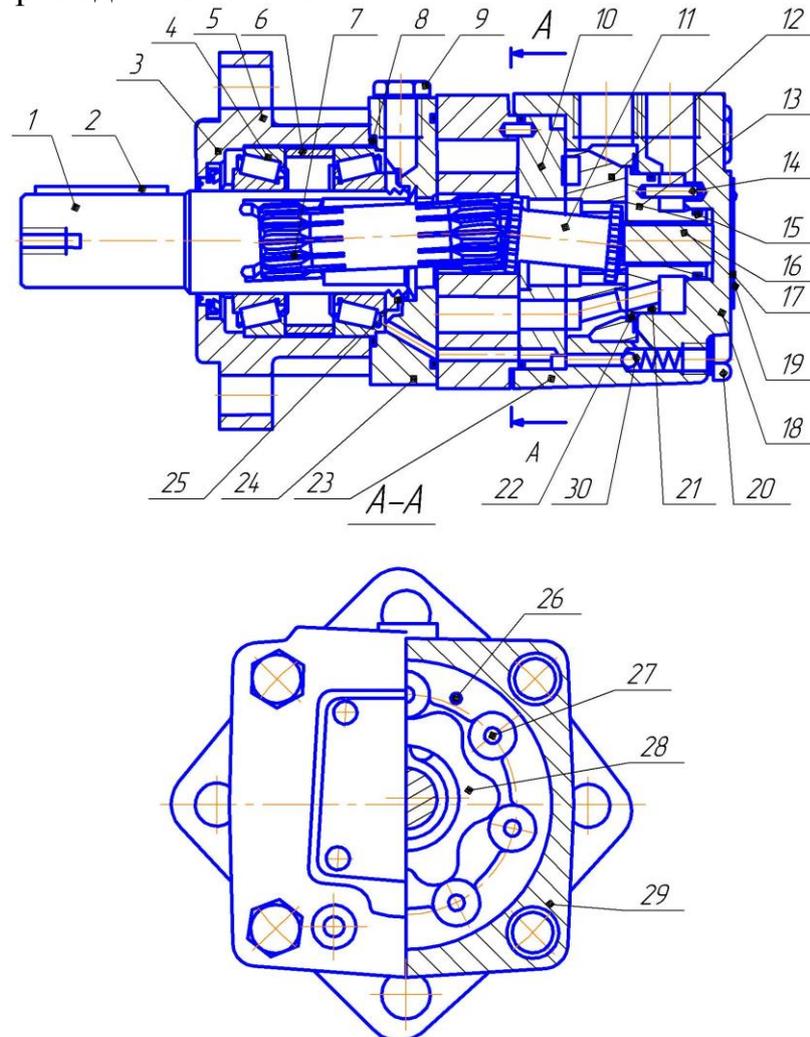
Планетарный гидромотор серии МГП: 1 – выходной вал; 2 – шпонка; 3 – манжета; 4 – подшипник; 5 – корпус; 6 – дистанционная втулка; 7 – зубчатый вал; 8, 15, 21 – резиновые кольца; 9 – пробка; 10, 12 – золотниковое устройство; 11 – вал; 13 – прижимающая втулка; 14, 26 – штифты; 16 – упорный ролик; 17, 18 – крышки; 19 – заклепка; 20 – болт; 22 – пружина; 23 – корпус золотника; 24 – пластина; 25 – гайка; 27 – ролик; 28 – ротор; 29 – статор; 30 – обратный клапан.
